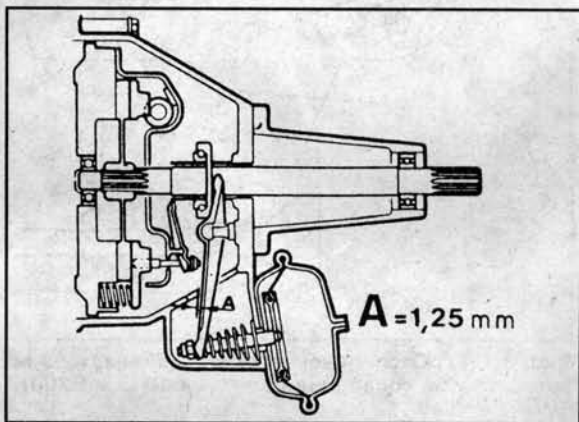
Регулировка сцепления, сопряженного с передачей CVT – установка положения разводящего рычага
